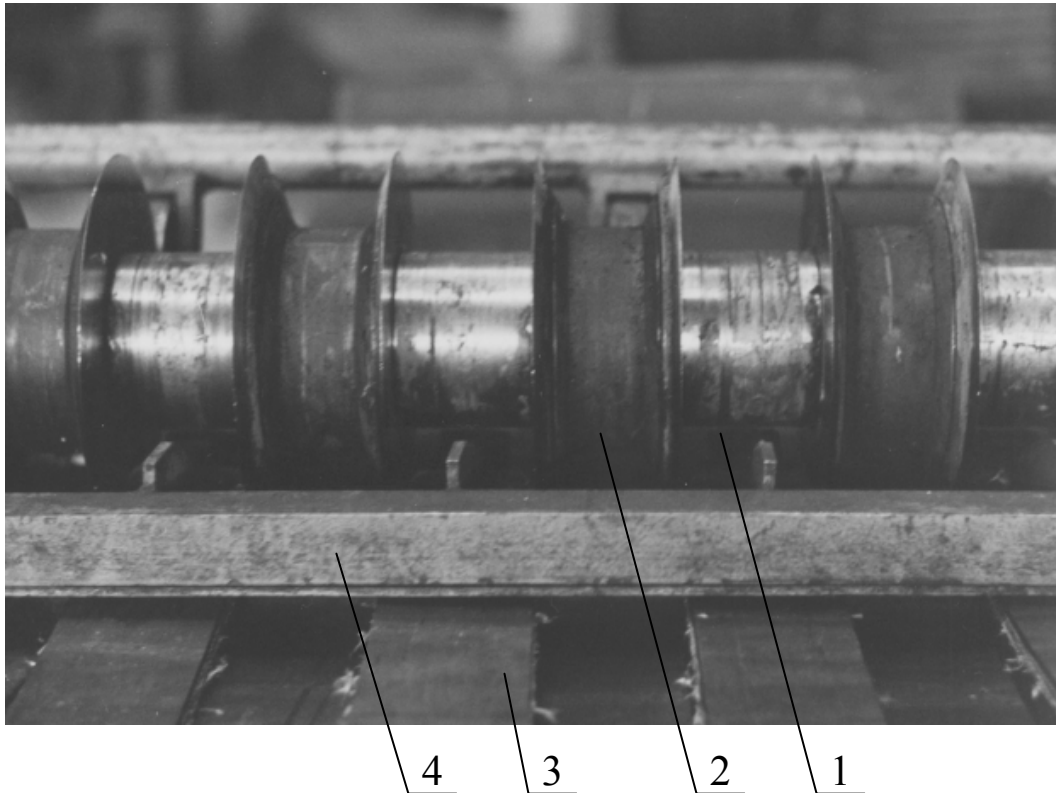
Ножовий блок верстату для порізки конвеєрної стрічки
